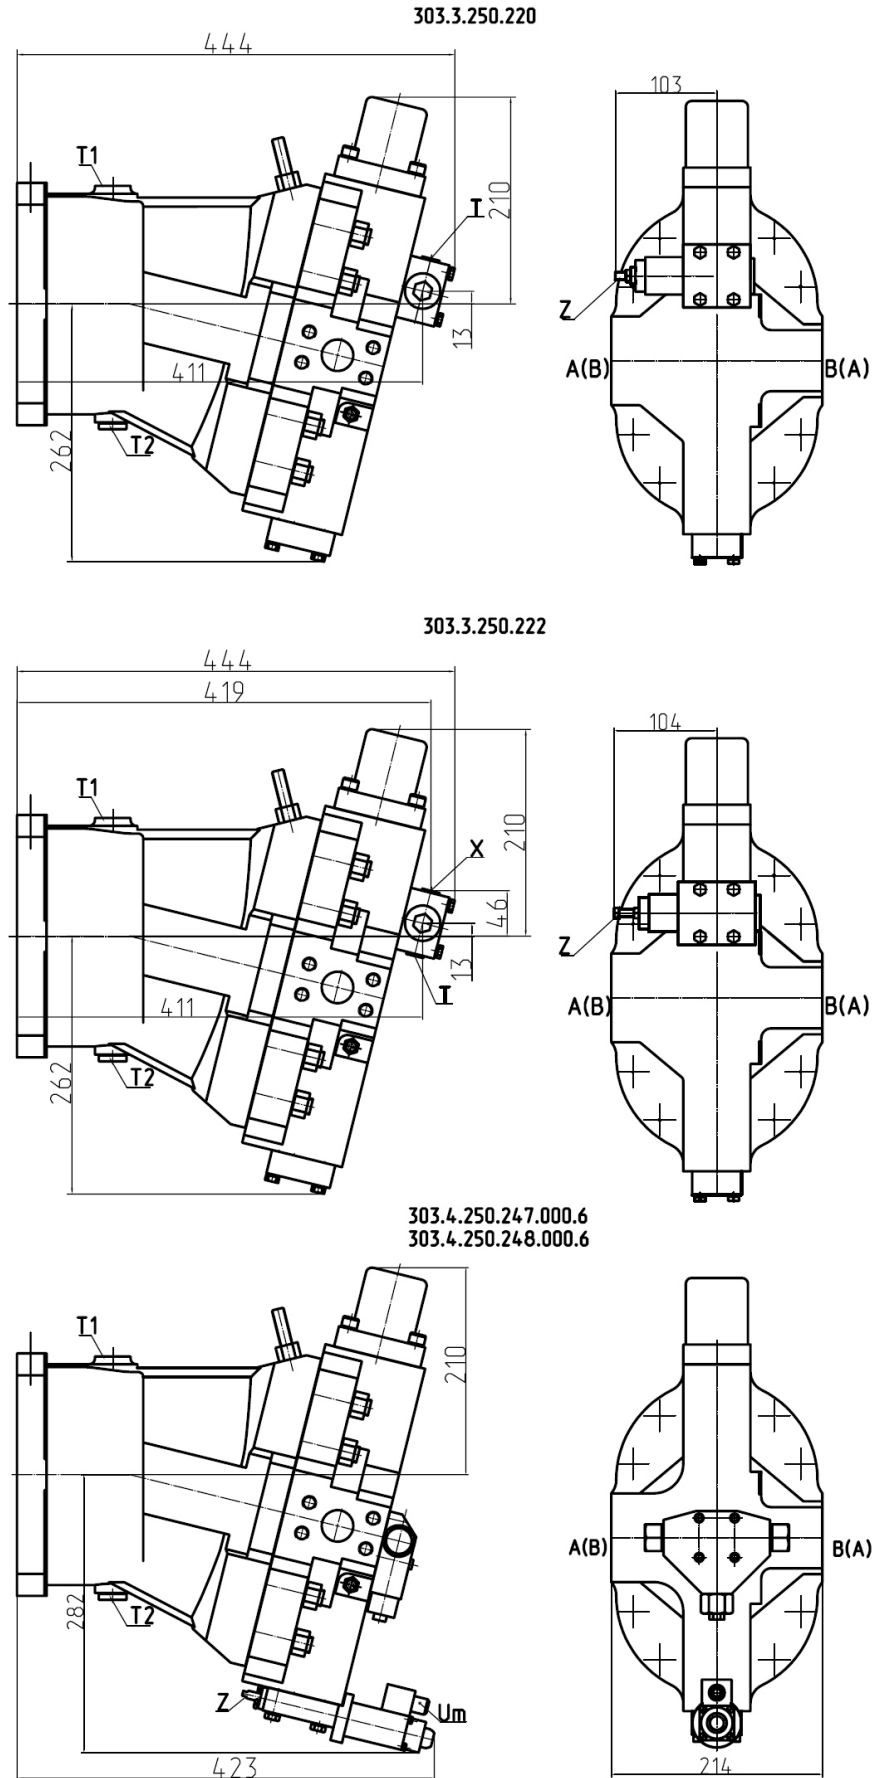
Габаритные и присоединительные размеры 303.3(4).250.
